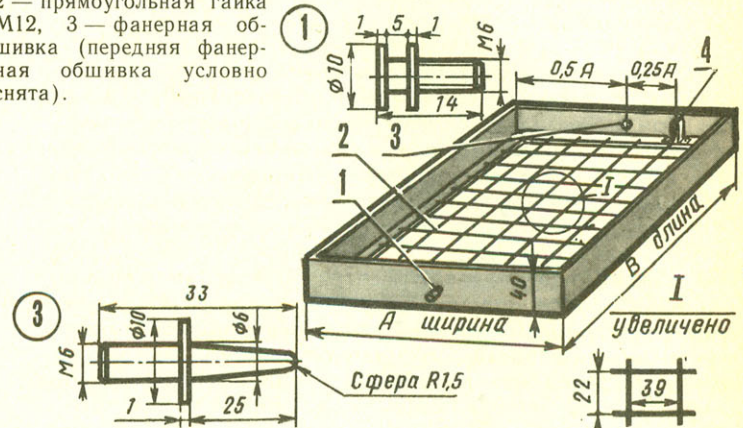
Лоток: 1 — передний шип, 2 — проволока  $\varnothing$  0,8—1,2 мм, 3 — задний шип, 4 — защитный кожух.
